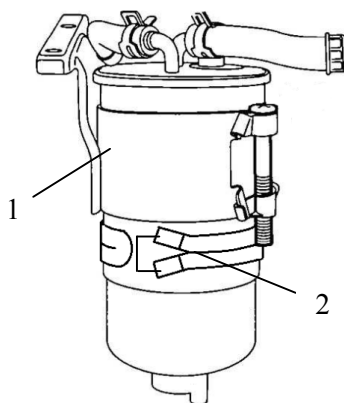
Ленточный подогреватель топлива в сборе с топливным фильтром: 1 – топливный фильтр; 2 – ленточный подогреватель.
